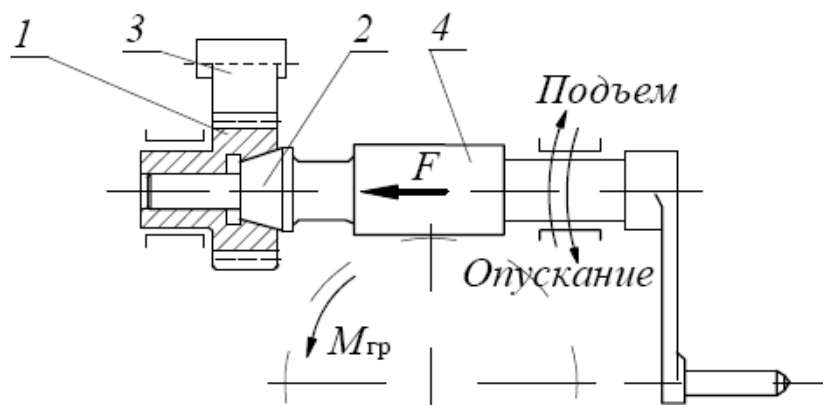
Грузоупорный тормоз с червячной передачей
